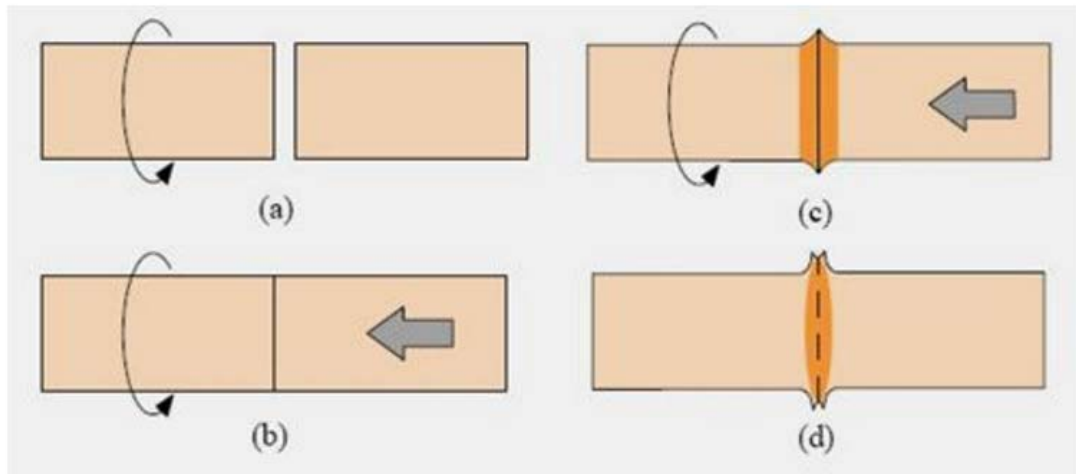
Tipo de soldadura por pressão, soldadura por fricção [52]
